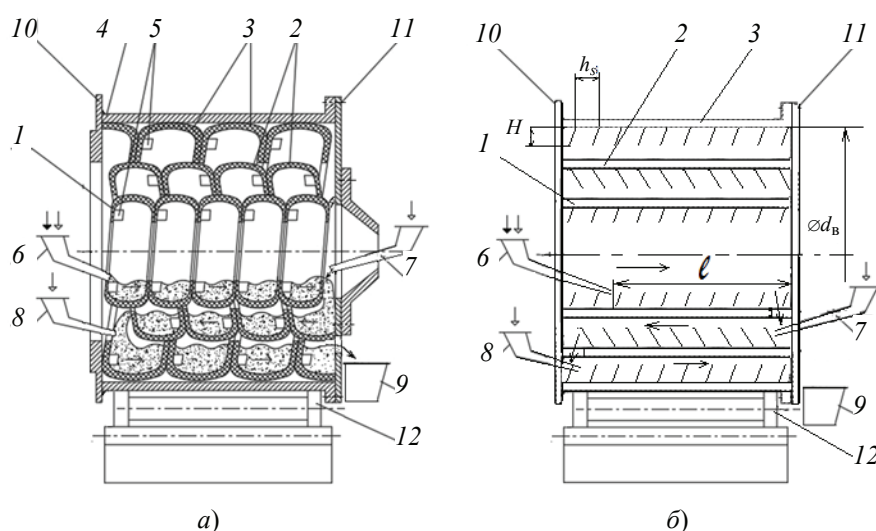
Схемы ступенчатого барабанно-винтового смесителя (а) и лабораторной установки (б)
